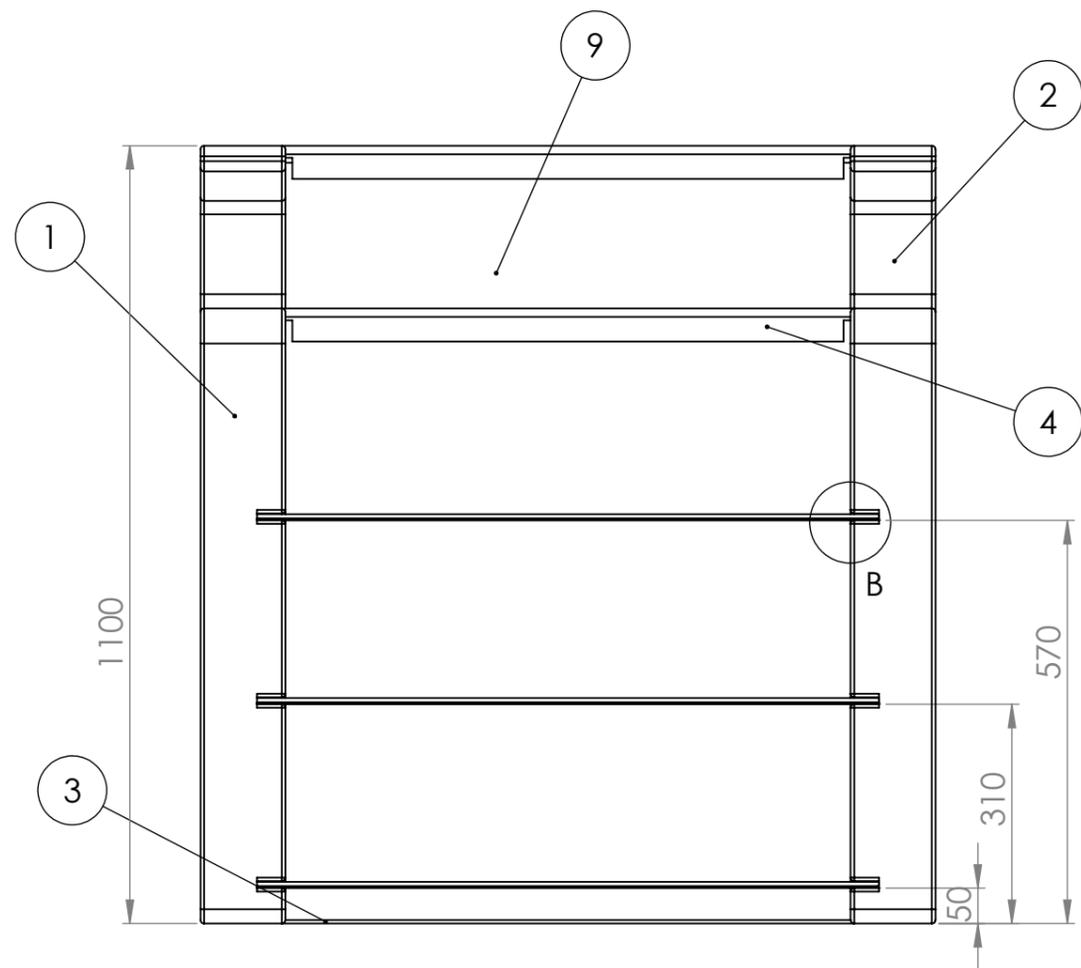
Paso 4 - Montaje Módulo Esquina
